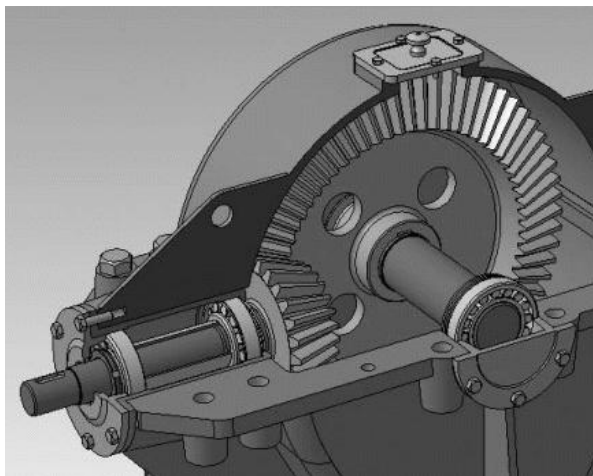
Загальний вигляд опорних вузлів шестерні та колеса конічної передачі
